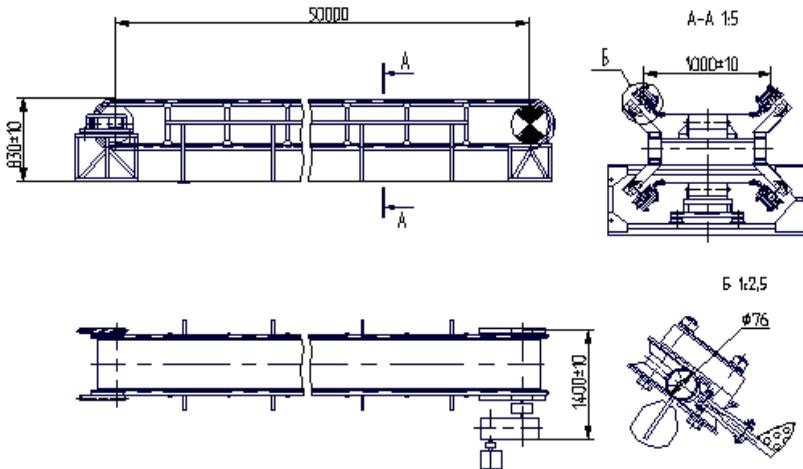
Фрагмент сборочного чертежа общего вида ленточного конвейера с подвесной лентой
